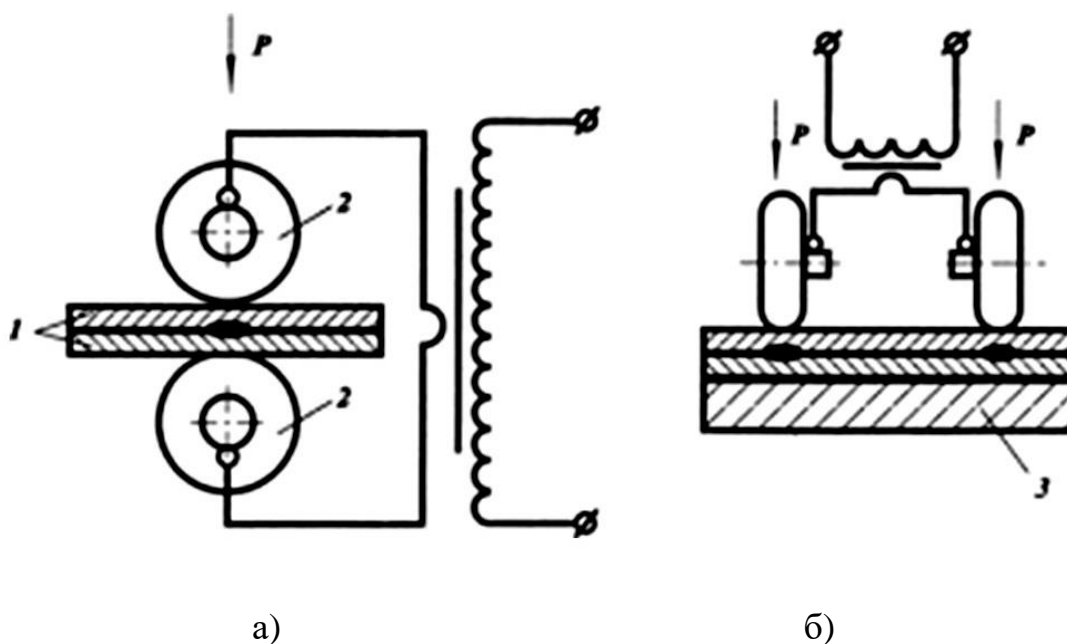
Схеми шовного зварювання: а – з нижнім катком; б – з нижньою плитою
